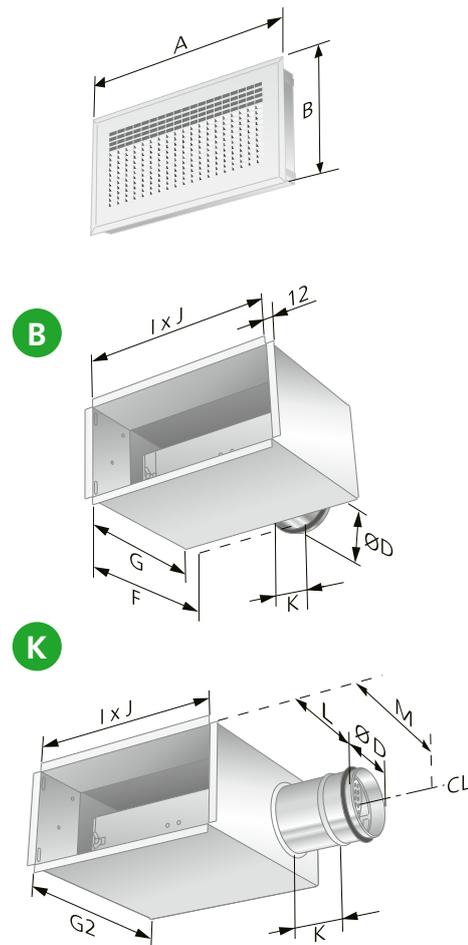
Abmessungen, LOCKZONE Wall und Anschlusskasten ALV.
